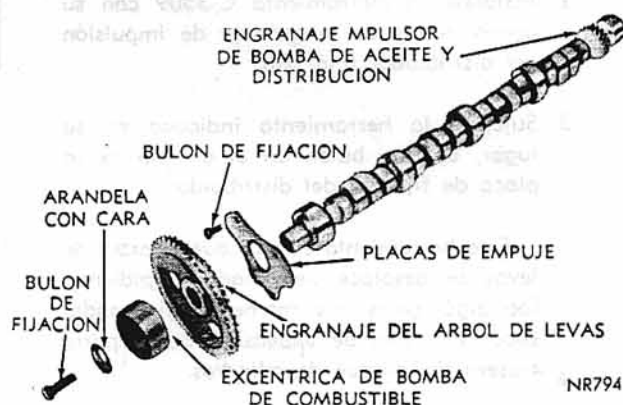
Conjunto de Engranaje y Arbol de Levas (Desmontada)
